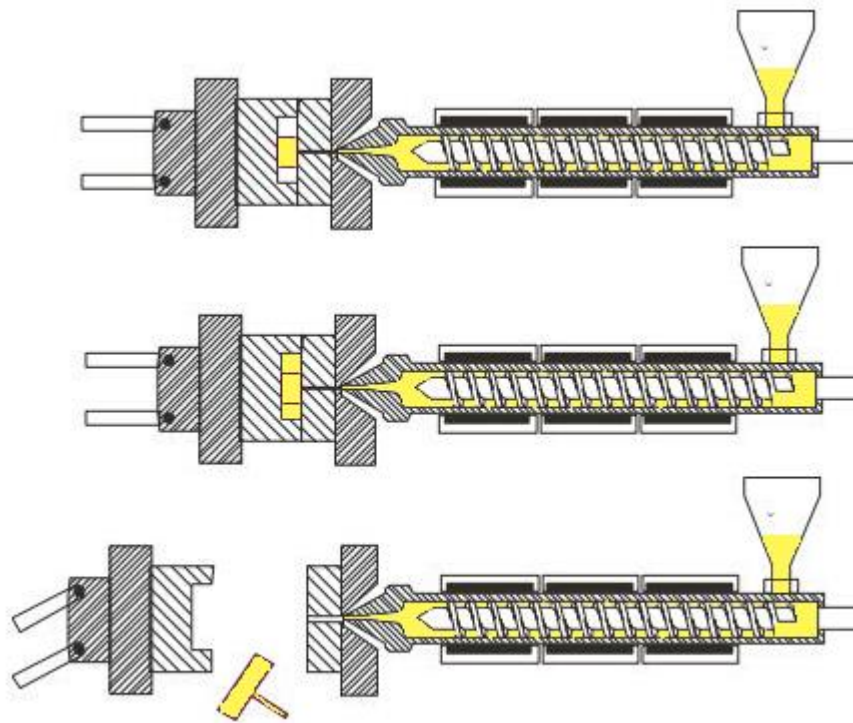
Secuencia de movimientos de la máquina inyectora durante el proceso de inyección del material dentro del molde.
